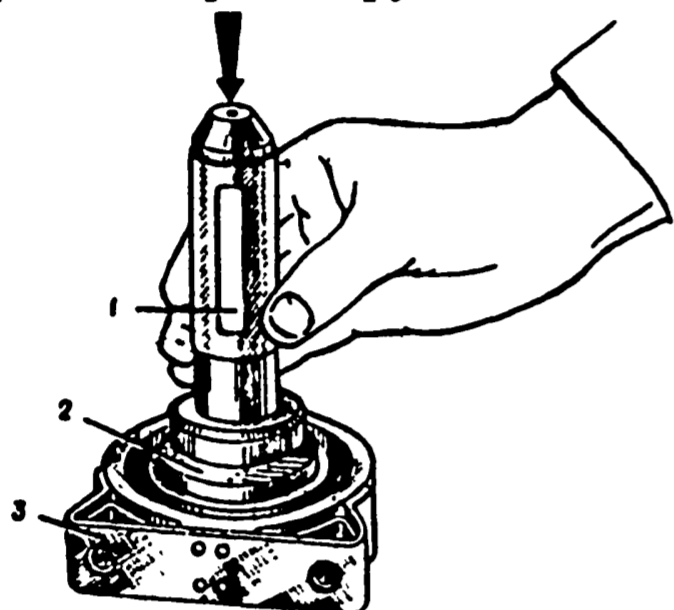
Запрессовка подшипника в упругую опору: 1 - оправка А.70045; 2 - подшипник; 3 - упругая опора
